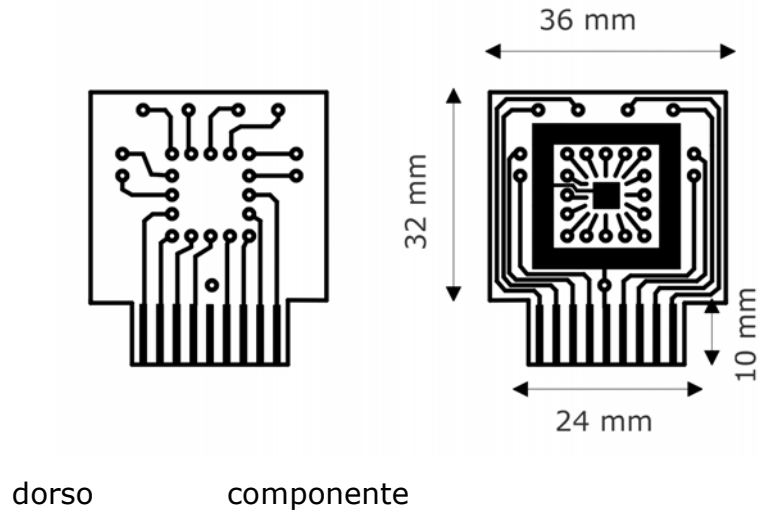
Esquema y dimensiones de la cara dorso y componente respectivamente de la placa PCB de doble cara diseñada.
